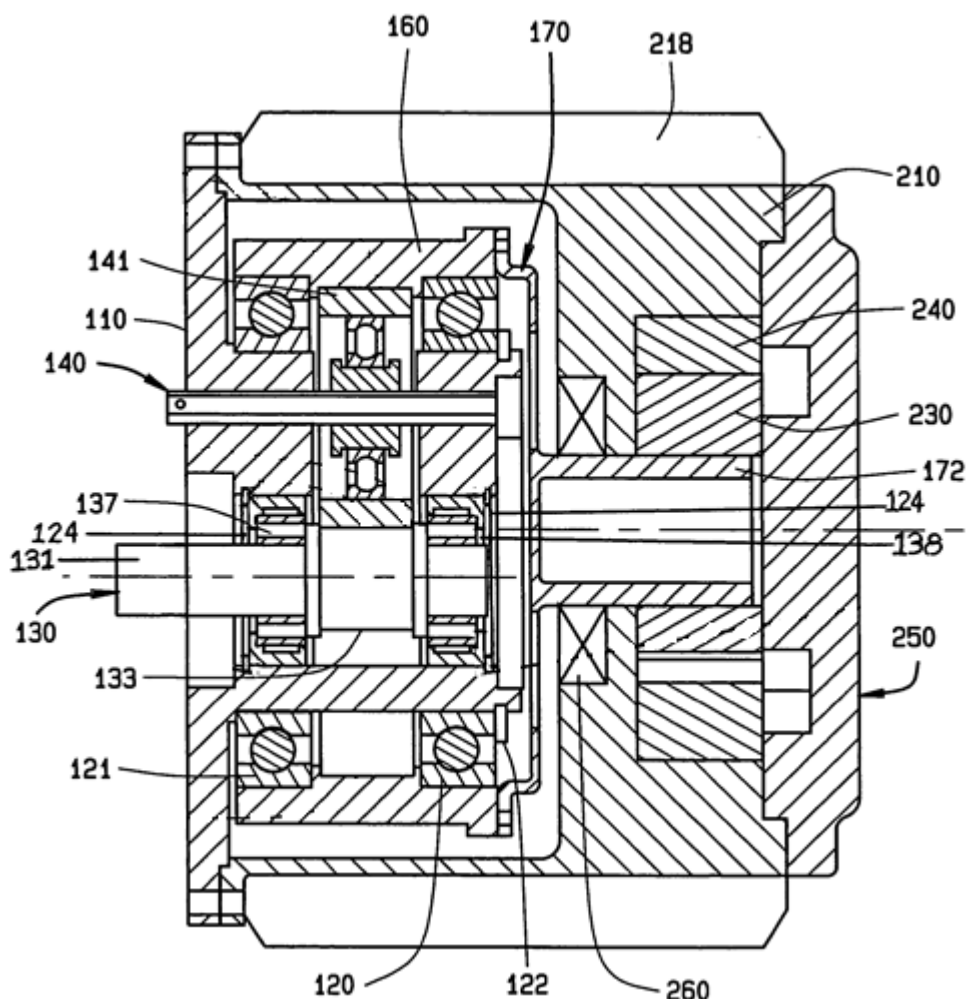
Интегрированный редуктор и насос: 110 – несущий элемент; 120,121 – шариковый подшипник; 122, 124 – стопорное кольцо; 130 –солнце; 131 – ролик солнца; 137,138 – роликовый подшипник; 140 –сателлит; 141 –ролик сателлита; 160 – внешнее кольцо; 170 –эпицикл; 172 – вал насоса; 210 – корпус; 218 – ребро; 230 – ротор; 240 –зубчатый кольцевой венец; 250 –крышка; 260 – уплотнение двунаправленного действия
